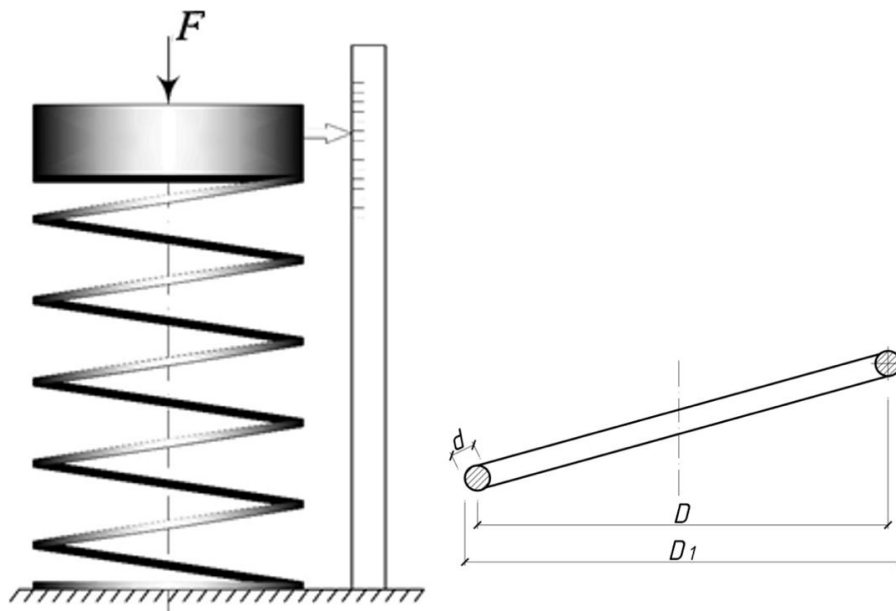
Схема установки для визначення осадки гвинтової циліндричної пружини
